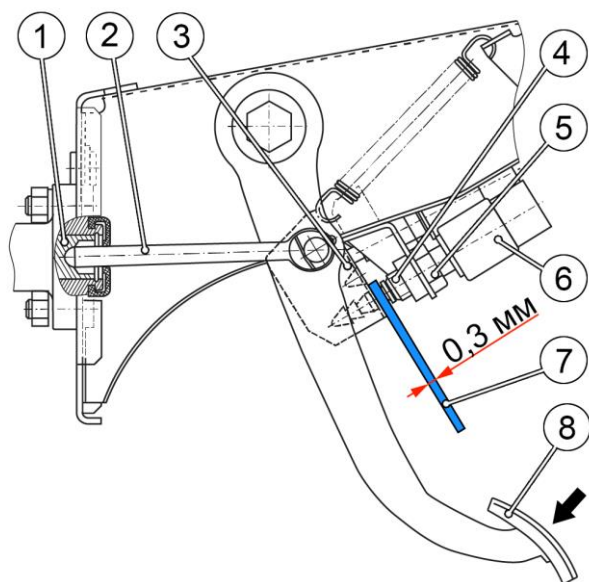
Установка выключателя сигнала положения педали сцепления: 1 - поршень цилиндра сцепления; 2 – толкатель; 3 - опорный кронштейн; 4 - головка подвижного штока выключателя; 5 - стопорная гайка; 6 - выключатель сигнала положения педали сцепления; 7 – щуп; 8 - педаль сцепления
